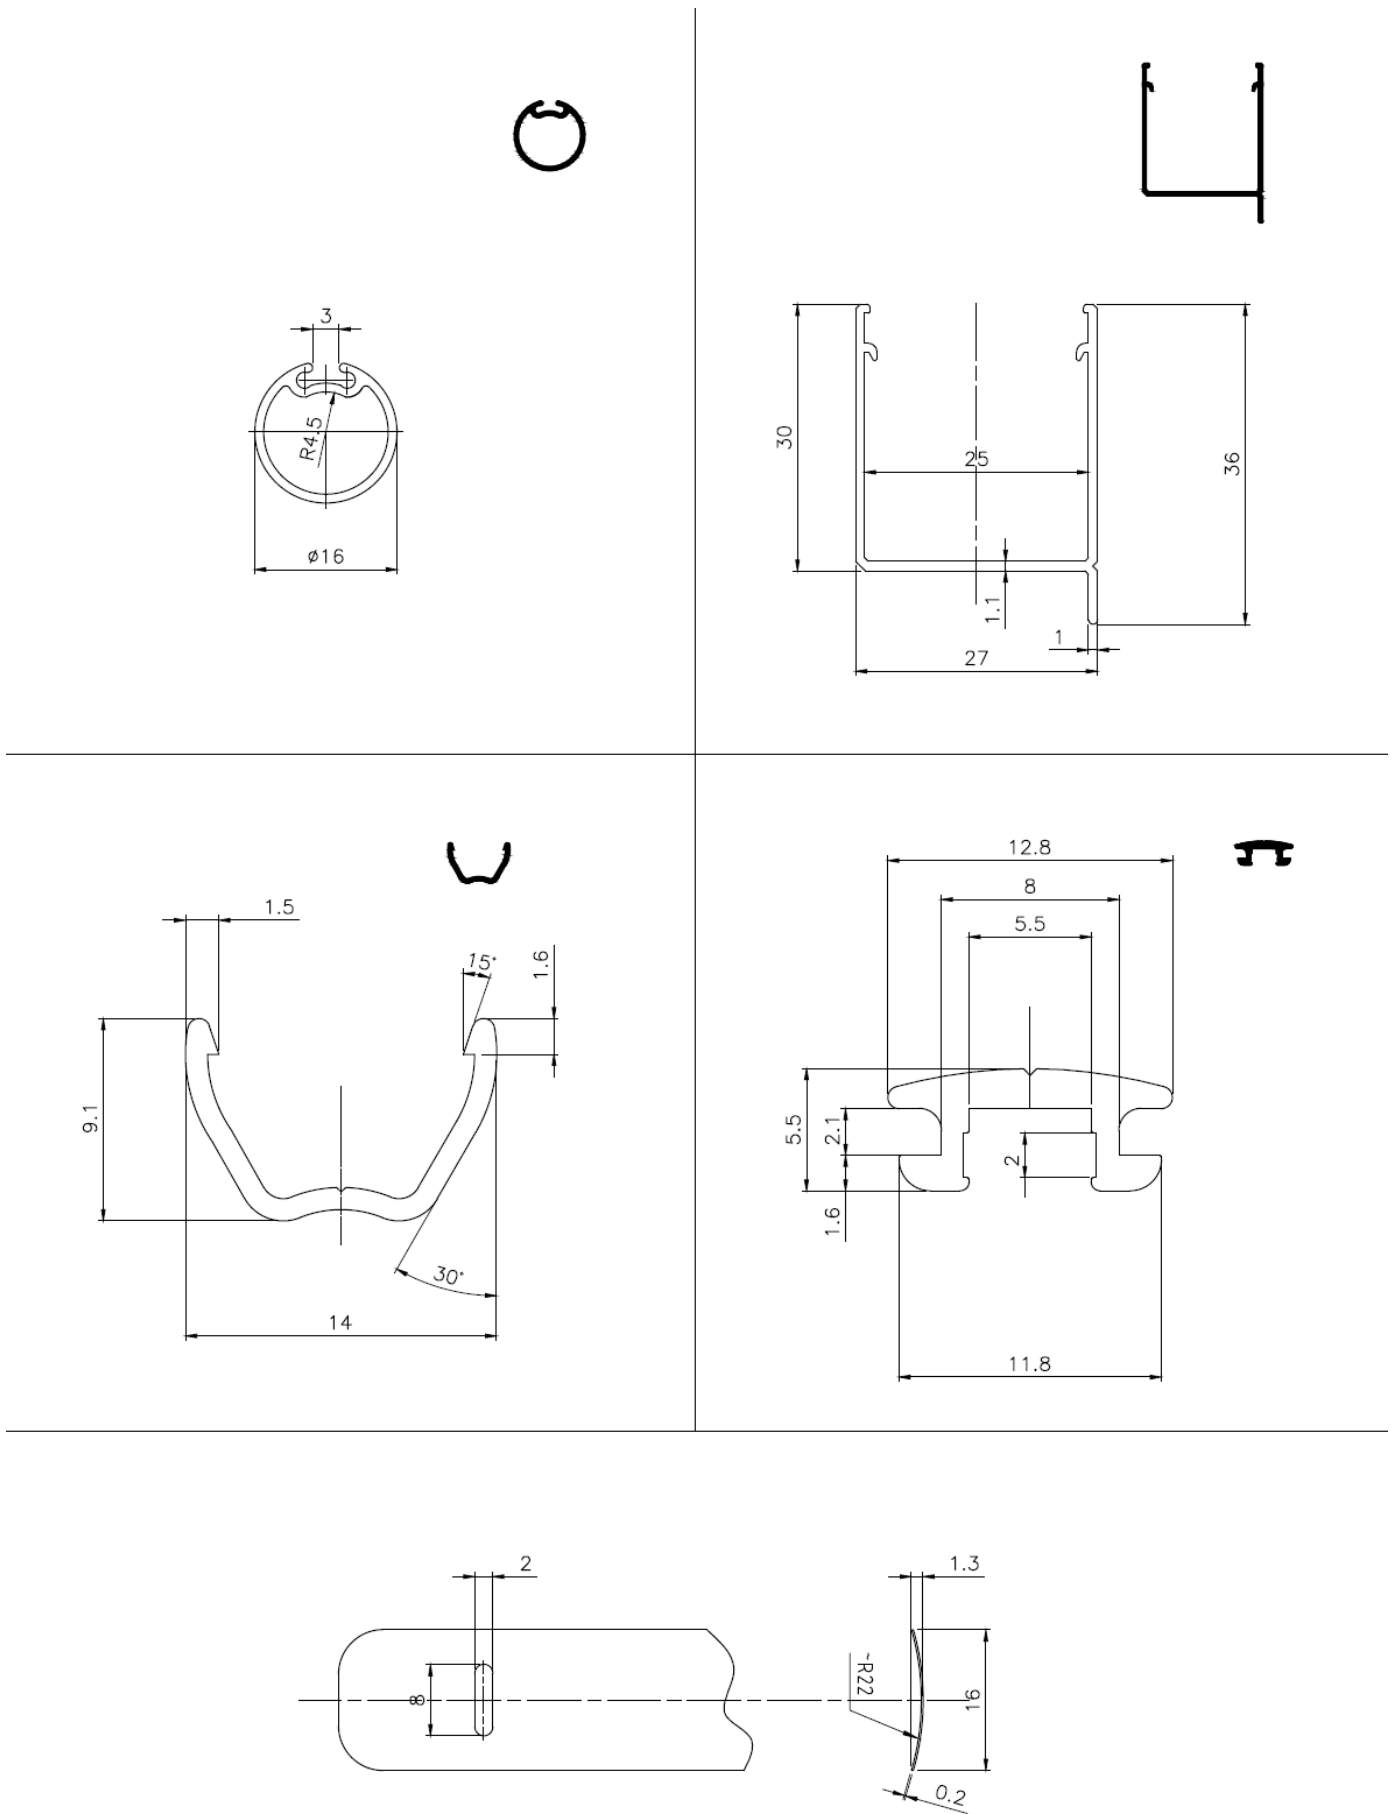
Tube d’enroulement – Caisson haut – Barre de charges (partie inférieure et partie supérieure) – Usinage lamelles
